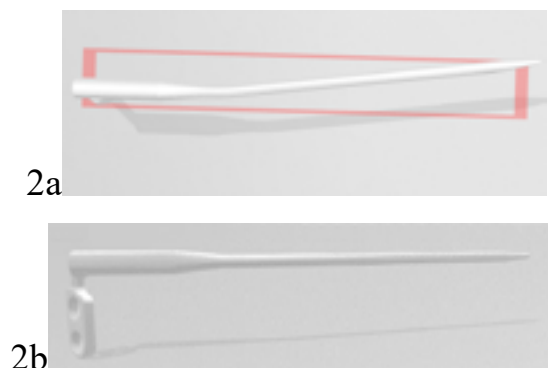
STL-модель стержня а – вид сверху б вид спереди
